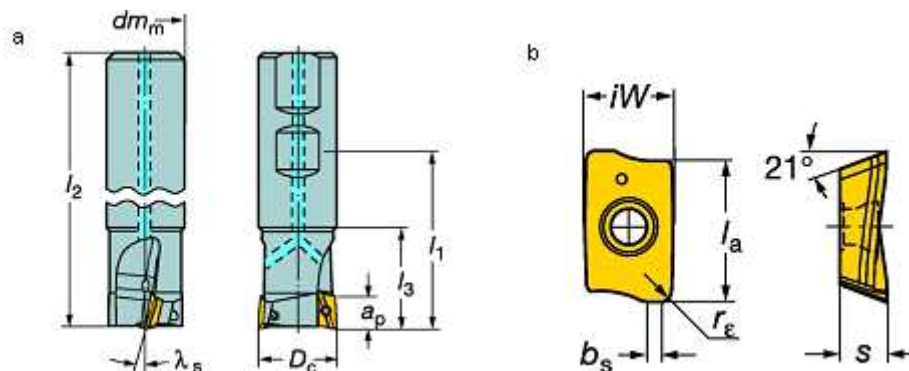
a) Fraise coromill 390, b) détails plaquette
